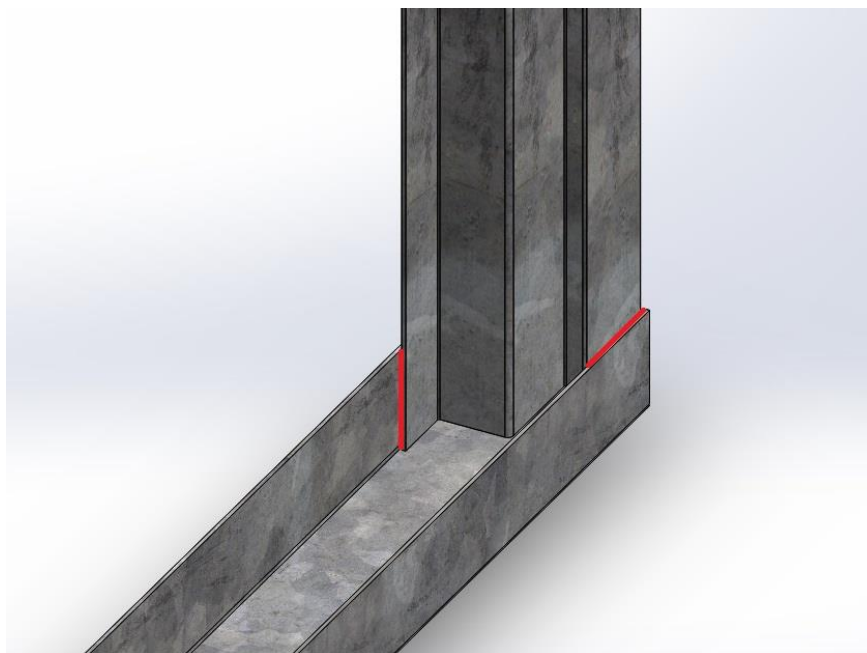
Ilustración de soldadura en esquinas del panel.
